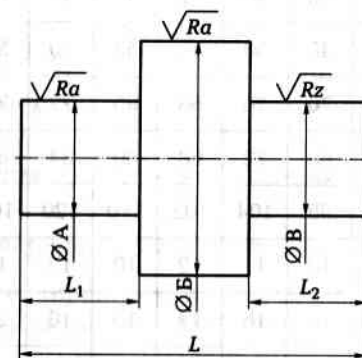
Эскиз обрабатываемой детали (вала)
